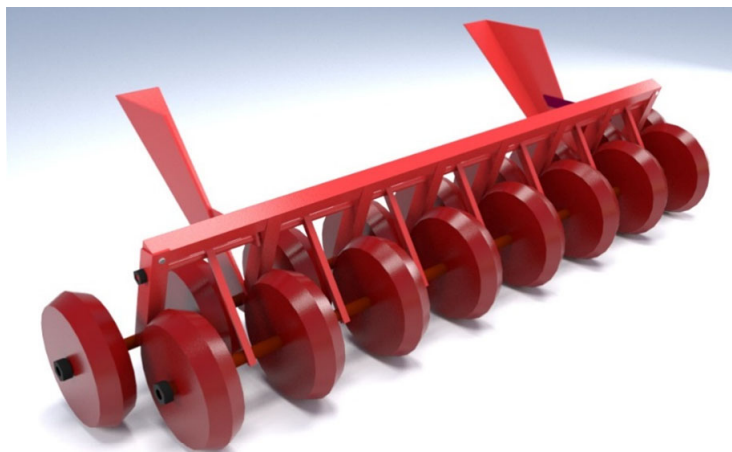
3D модель предлагаемых усовершенствованных двухрядных прикатывающих (уплотняющих) катков клиновидного типа
